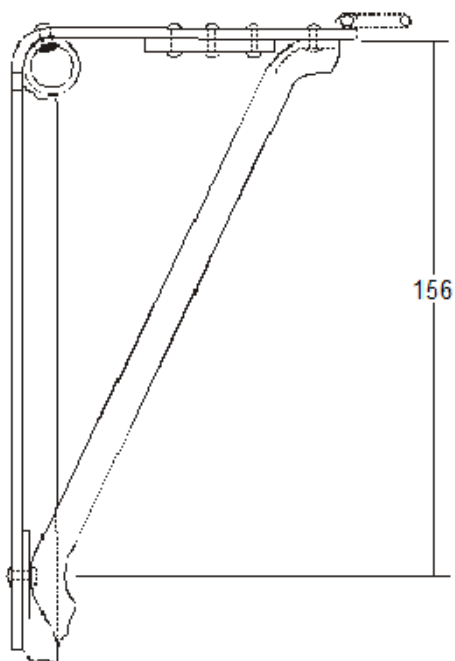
Vista da parte inferior do suporte metálico (medida em mm)
